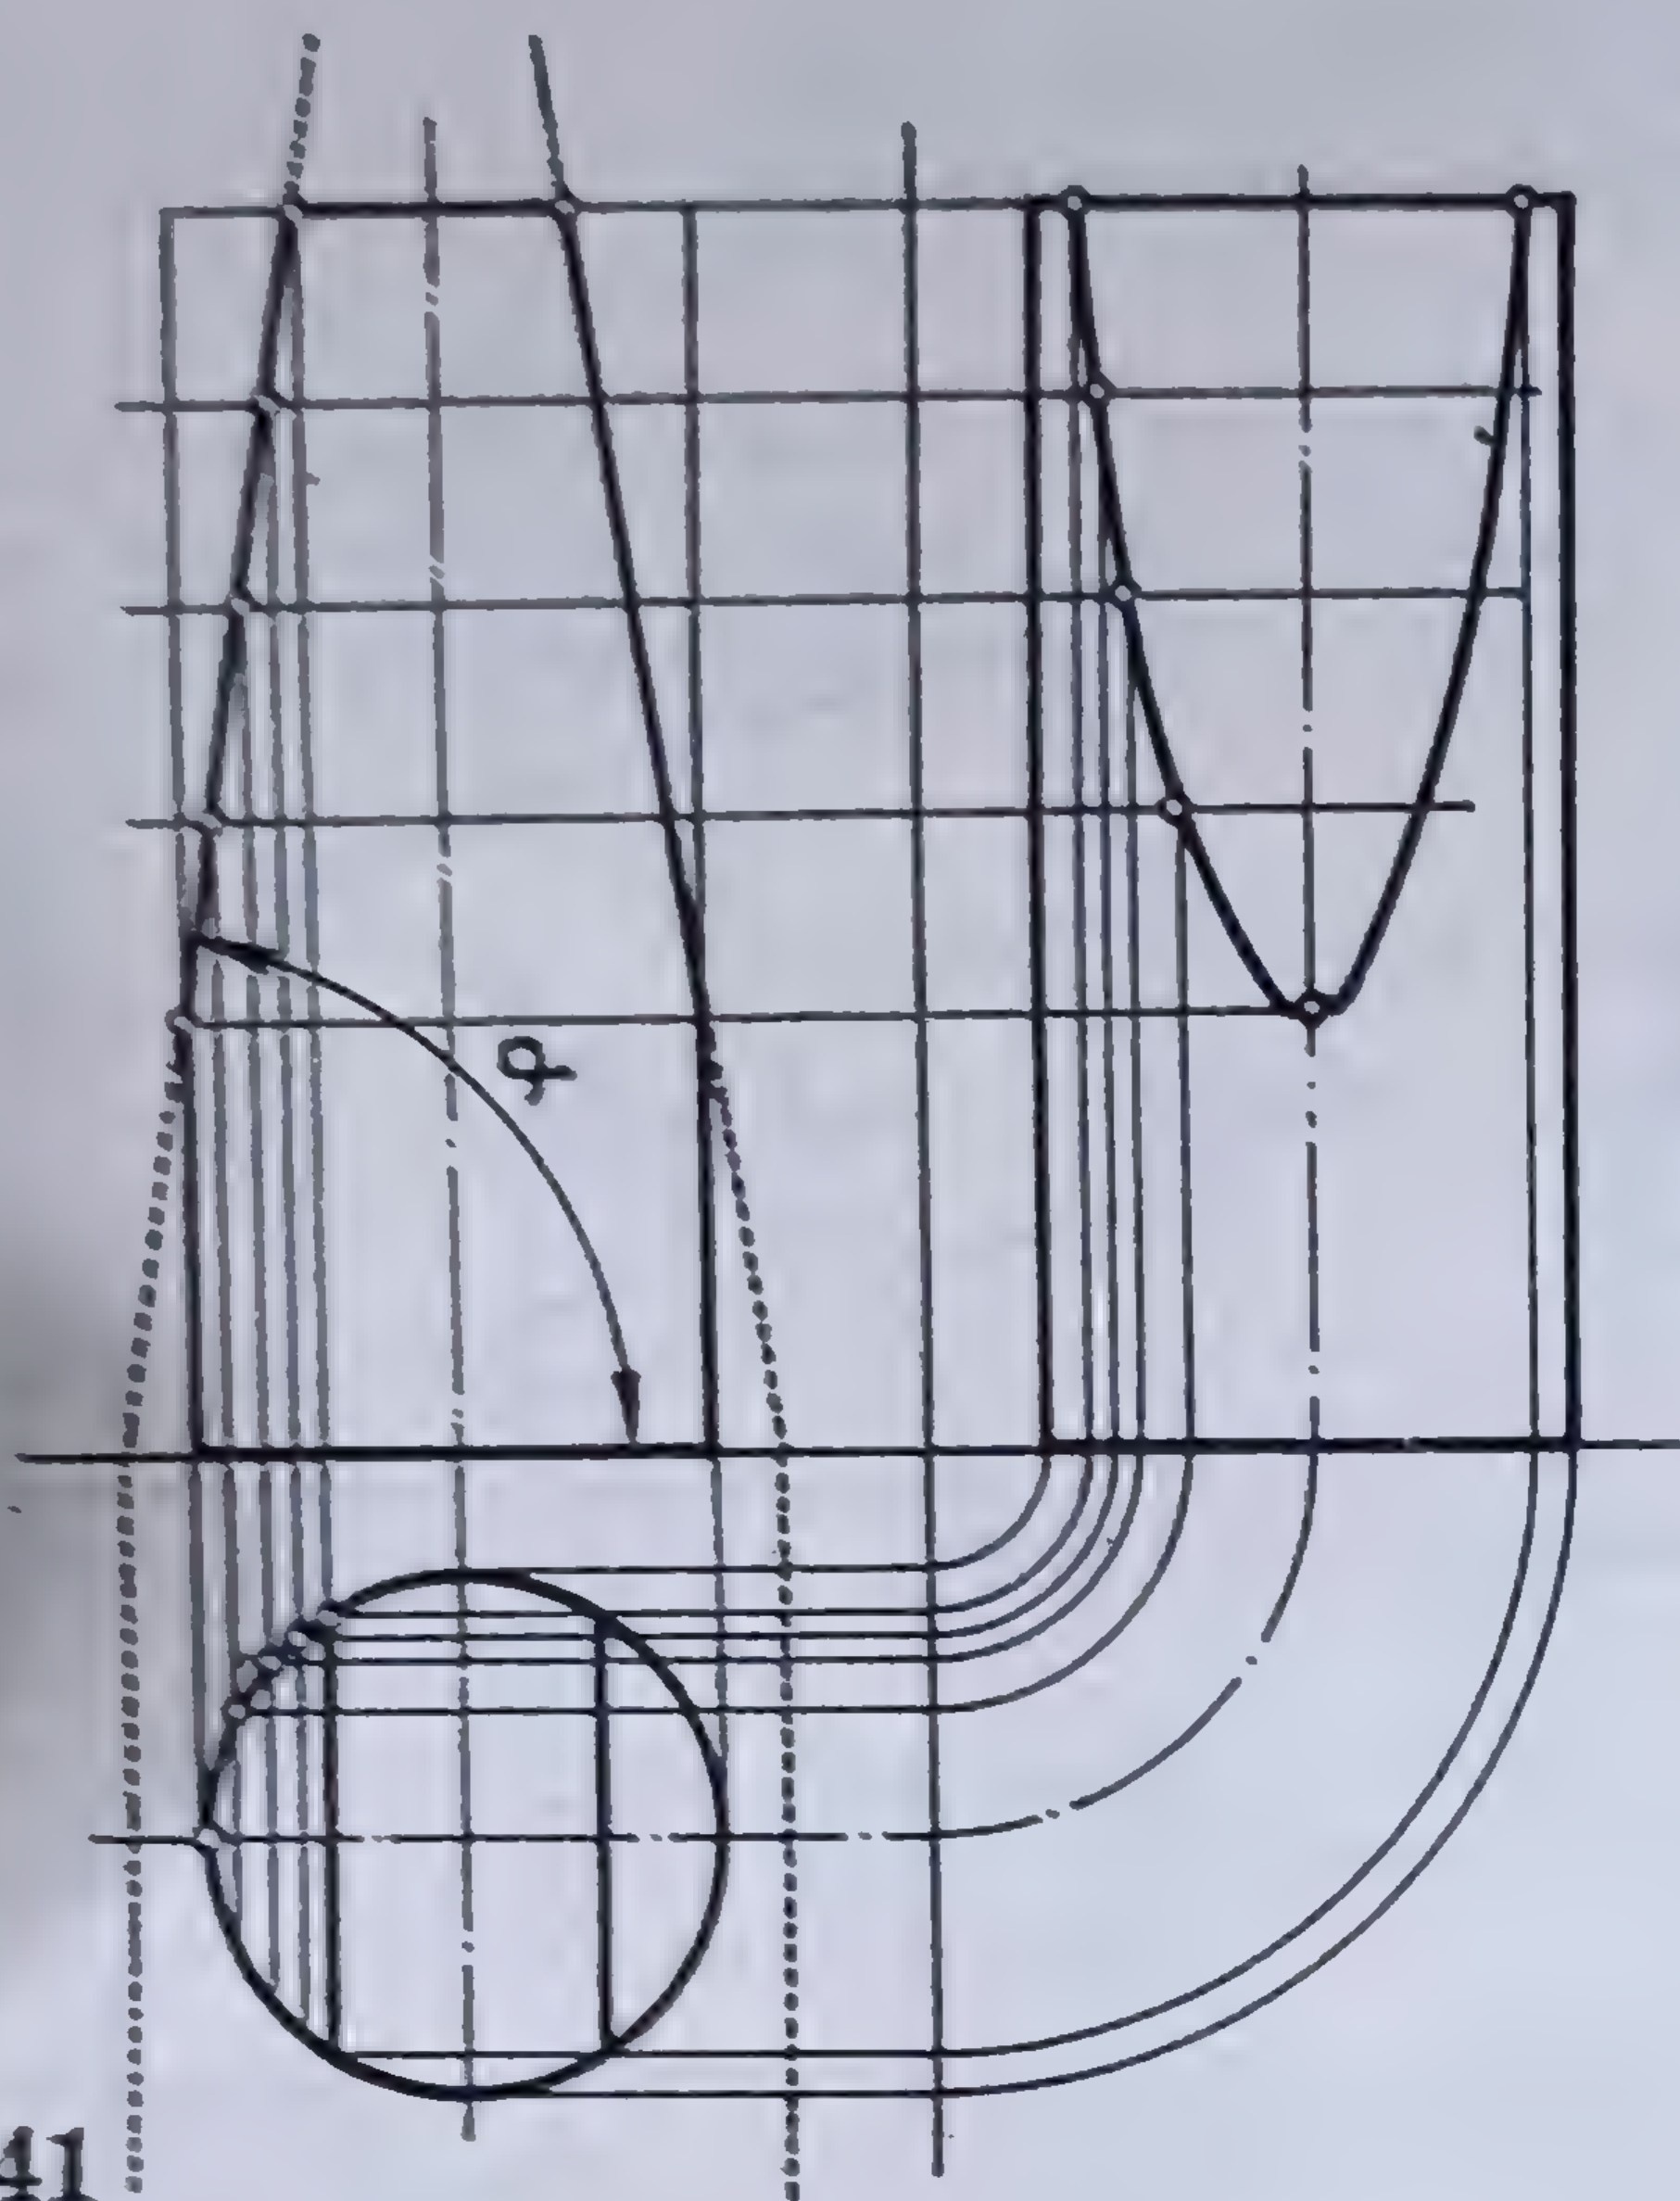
Formă constructivă cilindrică cu țesiri plane de la baza superioară.
